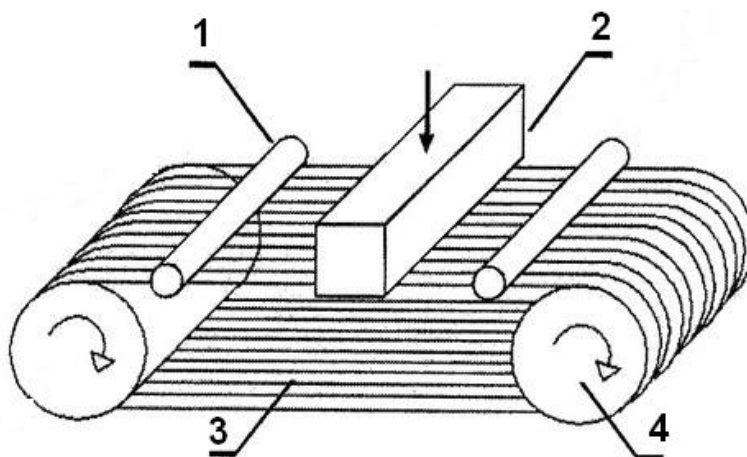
Схема розрізання мнокристалічної заготовки на пластини диском із внутрішньою ріжучою кромкою. 1 – стабілізуючий ролик, 2 – монокристалічна заготовка, 3 – ріжучі струни, 4 – привідний ролик.
